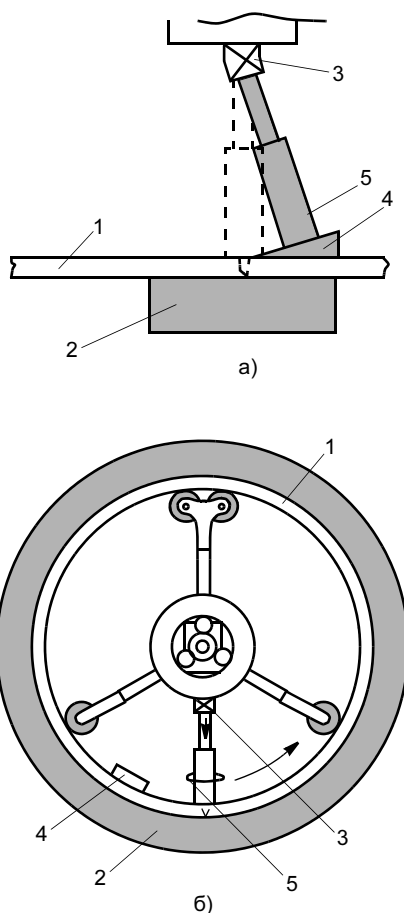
Схема СТП кольцевого соединения трубы: а, б — вид сбоку и вдоль оси трубы; 1 — труба; 2 — опорное кольцо; 3 — шарнирное соединение; 4 — остающаяся клиновидная пластина для окончания сварки без кратера; 5 — сварочная головка
